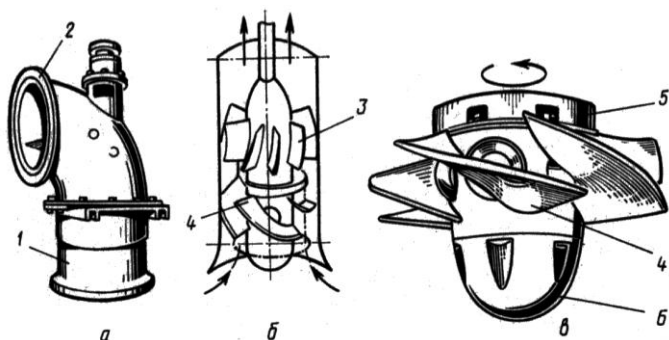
Осьовий насос (Ерхов М.С., Ільїн М.І, Місєнев В.С., 1991): а – зовнішній вигляд; б – схема; в – робоче колесо; 1 – всмоктуючий патрубок; 2 – напірний патрубок; 3 – апарат, що напрямляє струмінь води; 4 – лопать робочого колеса; 5 втулка; 6 – обтічник на вході.
